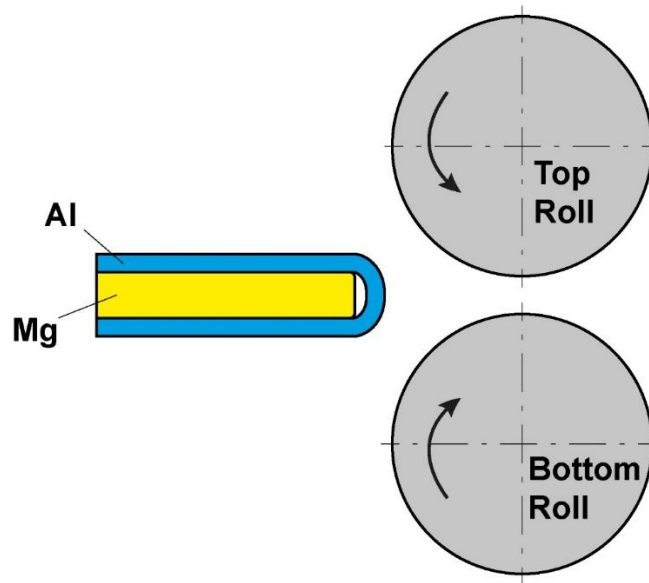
Схема прокатки тришарових пакетів на прокатному стані
